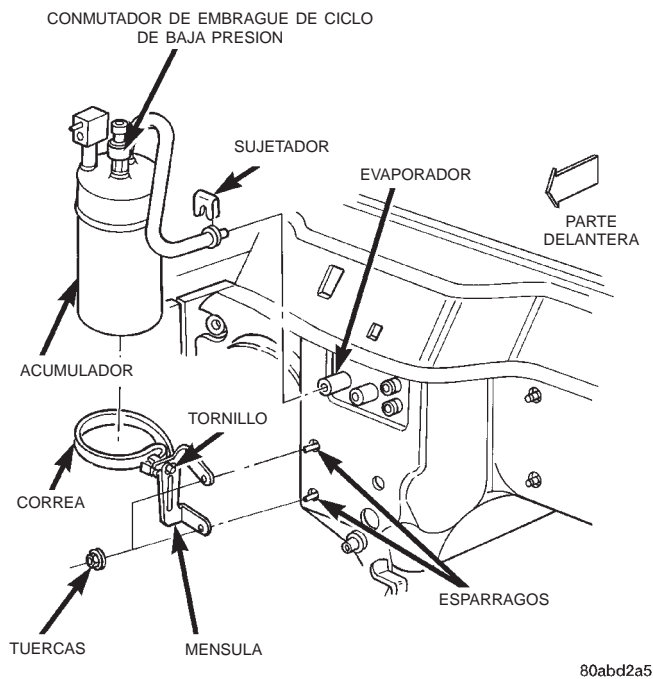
Desmontaje e instalación del acumulador, volante a la izquierda
